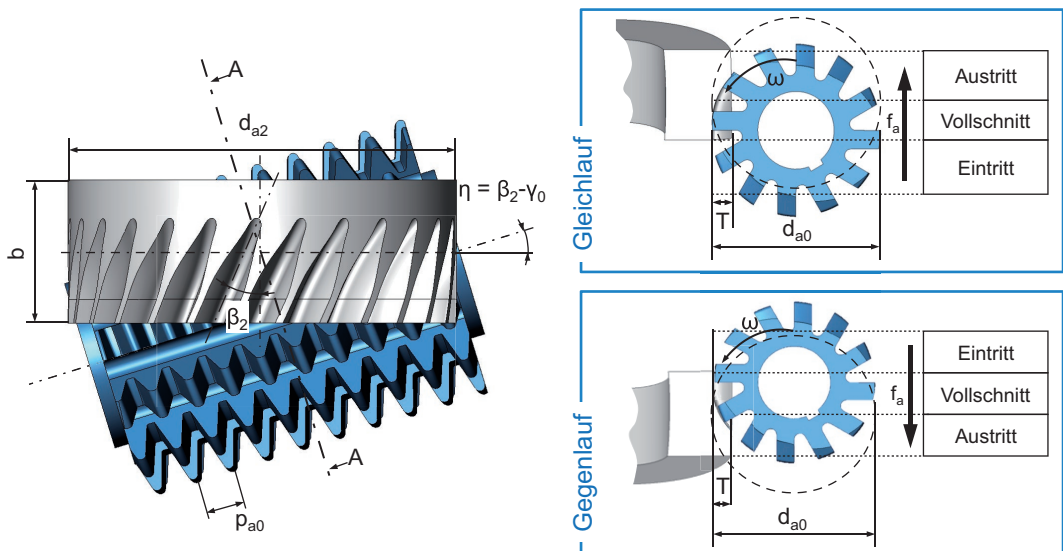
Bezeichnungen an der Paarung Wälzfräser - Werkrad
